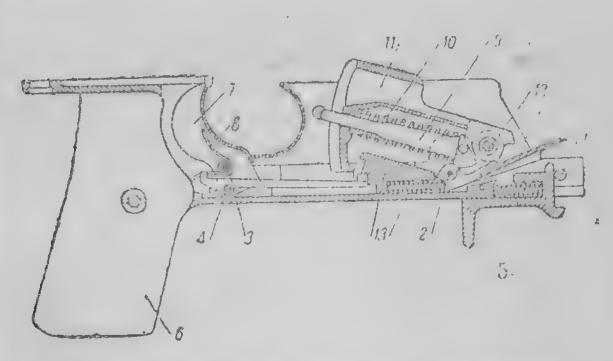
Коробна спускового механизма: 1—шинтька для креплення со ствольной коробкой; 2—ось автоспуска; 3—ось спускового крючка; 4—ось спускового рычага; 5—защелка магазина с пружиной; 6—рукоятка; 7—спусковой крючок; 8—пружина спускового крючка; 9—направляющий стержень боевой пружины; 10—боевая пружина; 11—курок; 12—ось курика; 13—шептало с пружиной; 14—автоспуск
